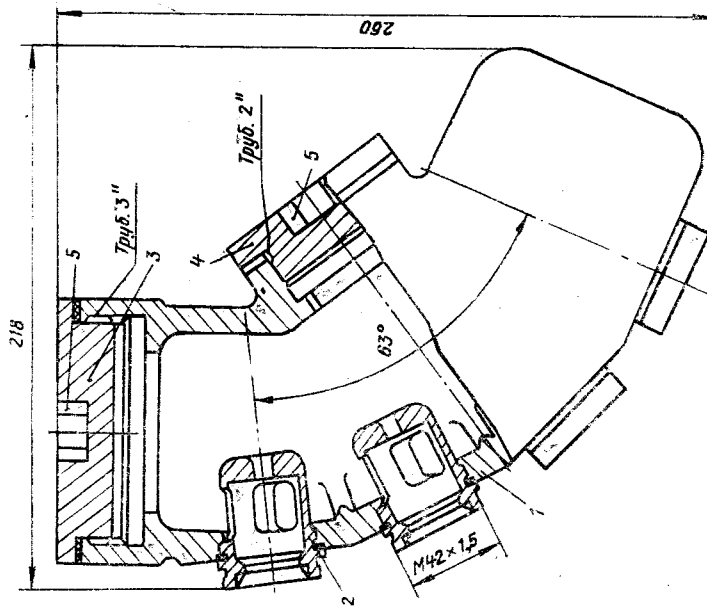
Насадок комбинированный центробежный четырехставочный НКЦ-4 (черт. С1313, ВНИИПО): 1 — корпус; 2 — распылитель центробежный РЦ; 3 — заглушка отверстия Труб.3"; 4 — заглушка отверстия Труб. 2"; 5 — отверстие под ключ 7218-0383 40ХФА Н12Х1 (ГОСТ 11737—74)
